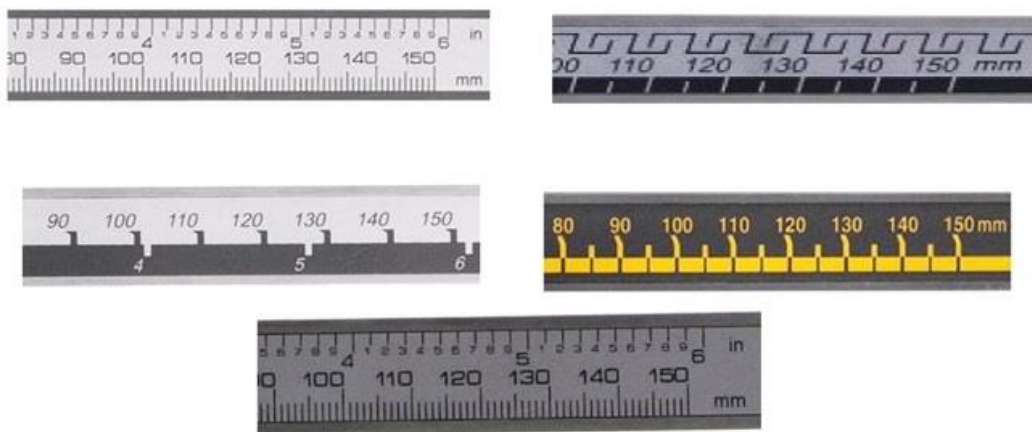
Внешний вид штанги штангенглубиномеров
